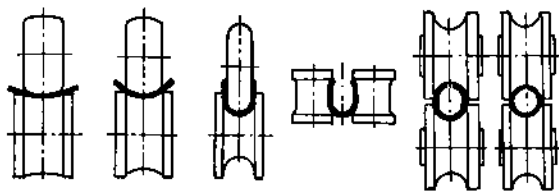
Последовательность процесса свертывания трубы из полосы в шести вальках профиле-загибочного станка
